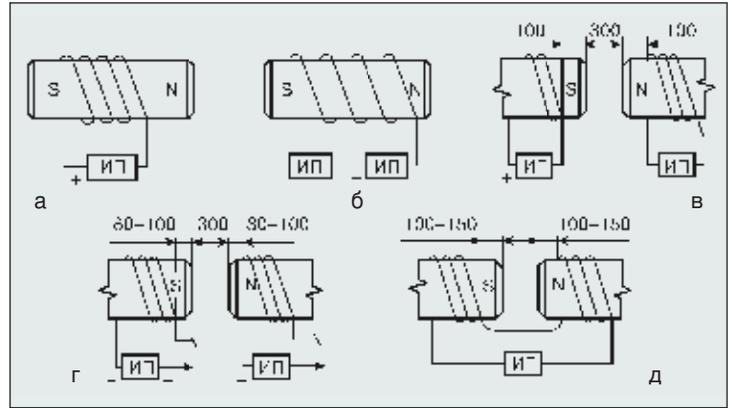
Схема проведения размагничивания постоянным током: а — по типовой методике с использованием одного сварочного преобразователя; б — по типовой методике с использованием двух последовательно соединенных сварочных преобразователей; в — размагничивание концов труб; г — по методике с разрывом магнитной цепи; д — по методике размагничивания собранных стыков труб (ИП — источник питания (сварочный преобразователь))
